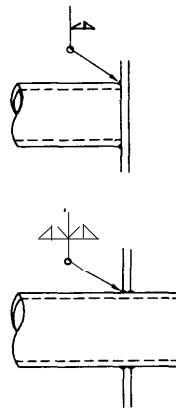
単一鋼管部材の端部の溶接方法 ($d \leq l/25$)
